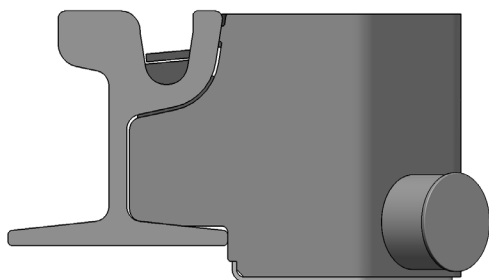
Type SK420-011 (Schienenprofil Ri55; geschweißt)
